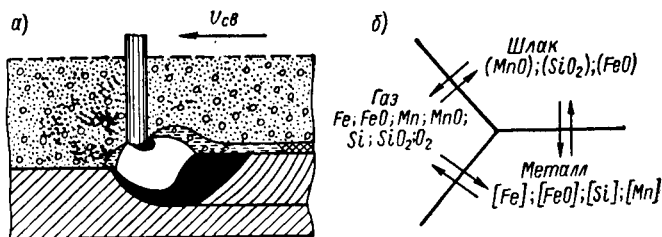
Общая схема взаимодействия металла с газами и шлаком при автоматической сварке под флюсом: а — продольный разрез через сварочную ванну; б — схема взаимодействия металл—шлак—газ
